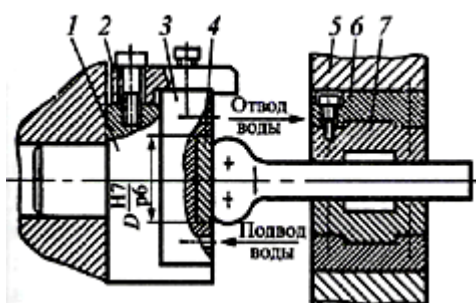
Конструкция рабочего инструмента для свободной электровысадки: 1-4-опорный электрод; 5-7-радиальный электрод.
